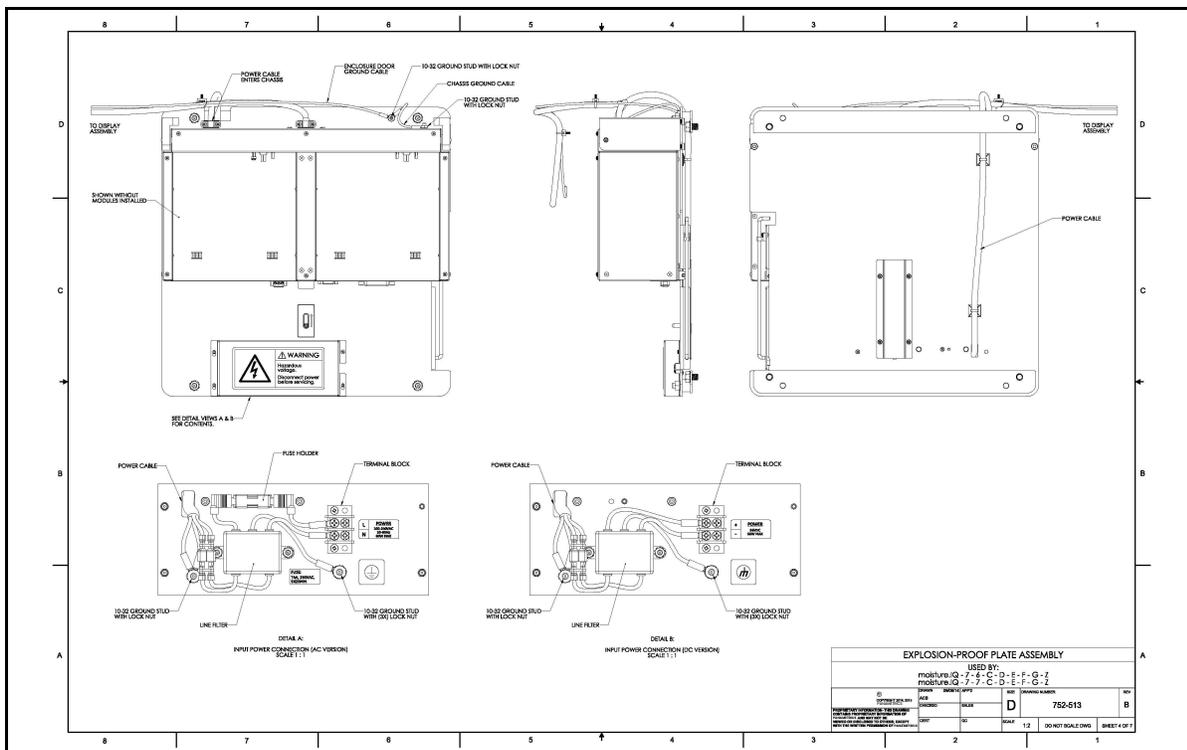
Montageplatten-Baugruppe für explosionsgeschützte Version
